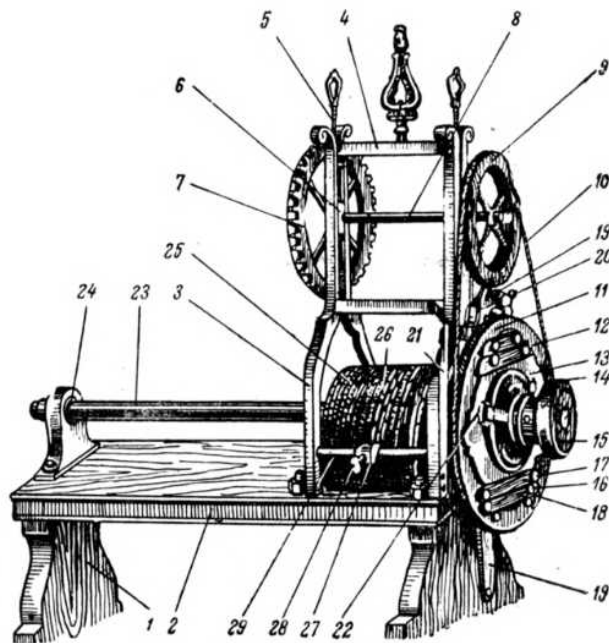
Кинематическая схема гильоширного токарно-овальерного станка А. К. Нартова 1722 г., составленная для станка в том виде, как он находится в Государственном Эрмитаже (по А. С. Бриткину).
